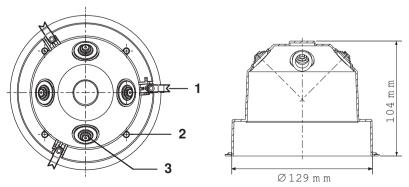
Vues en plan et de côté du boîtier arrière pour montage au plafond FAA-500-BB
